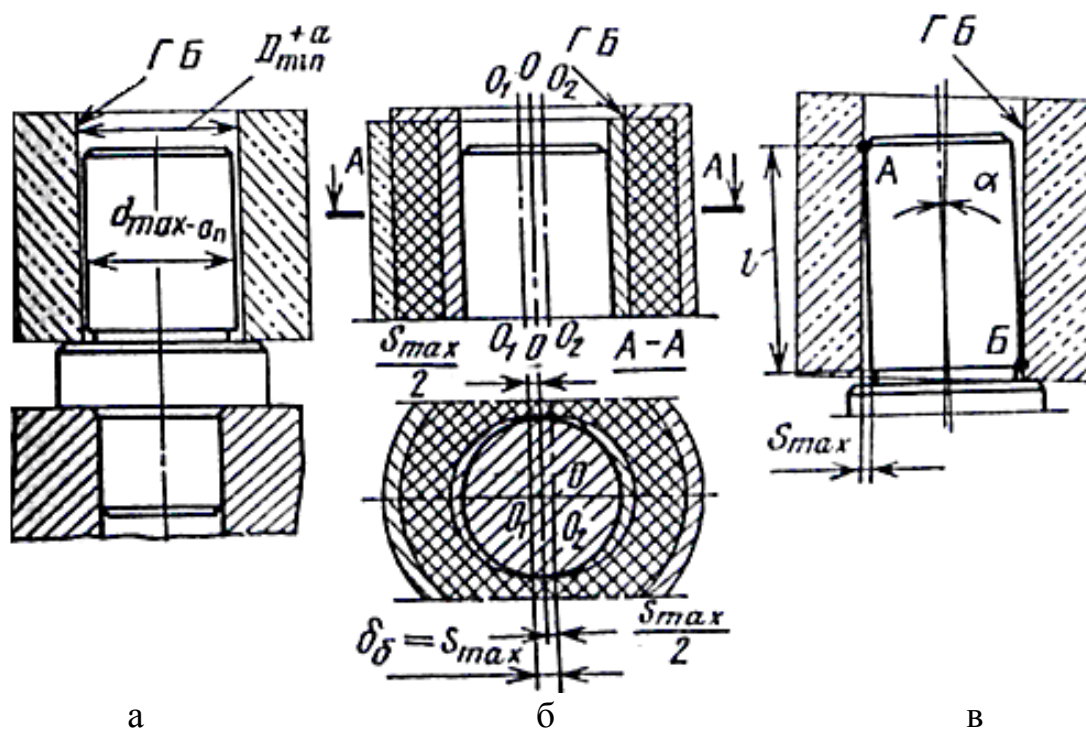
Схема базирования с главной базой, имеющей форму цилиндрического отверстия, на цилиндрическую оправку (палец).
